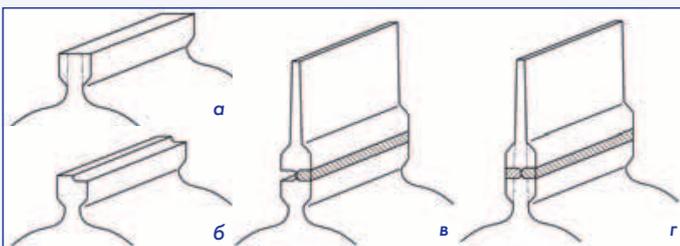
Способ ремонта монокопел с использованием лазерной сварки: а) привулочная часть диска; б) выполнение углублений; в) заполнение углублений; г) подготовленный к сварке стык
